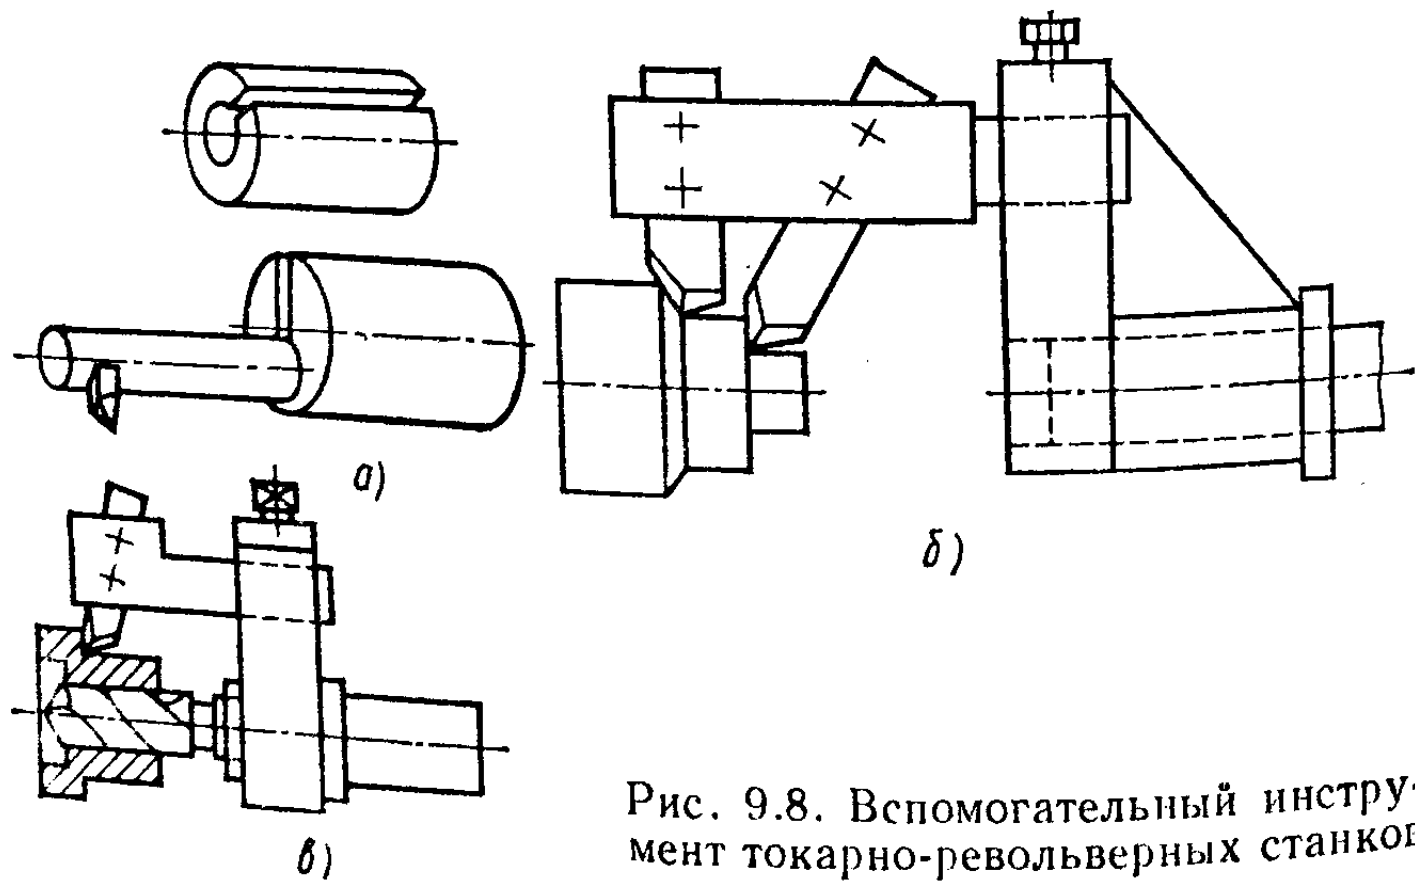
Вспомогательный инструмент токарно-револьверных станков
